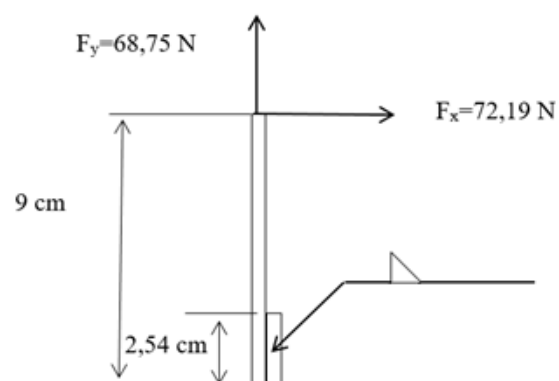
Diagrama de cuerpo libre de la unión soldada A. Se puede observar las dimensiones y componentes de la fuerza que actúan sobre la unión.
